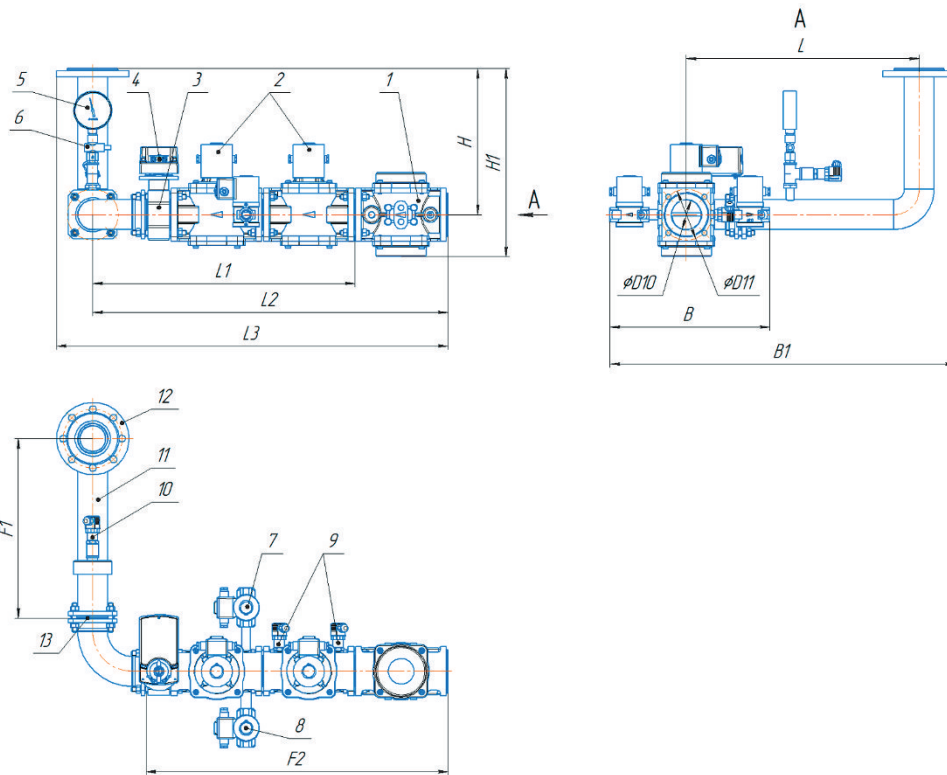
Габаритный чертеж газовых линий (размеры смотри таблицу 12).
